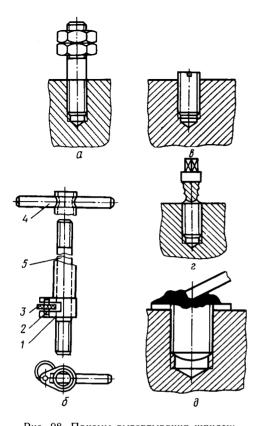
Приемы вывертывания шпилек: a-c помощью двух гаек; 6- эксцентриковым ключом; в- посредством шлица под отвертку; e-c помощью экстрактора; d-c помощью приваренного прутка; I- корпус; 2- ось; 3- рифленый ролик; 4- вороток; 5- шпилька
